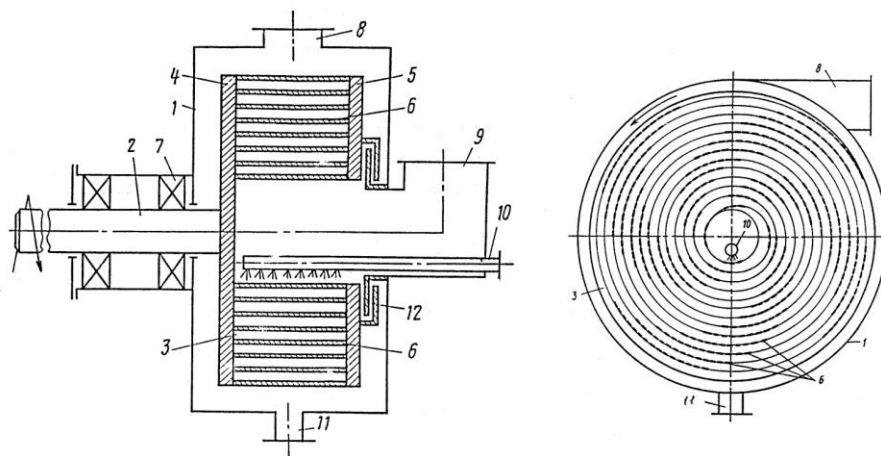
Скоростной роторный центробежный теплообменный аппарат [85]. 1 – корпус; 2 – вал; 3 – ротор; 4, 5 – торцовые крышки; 6 – лопатки; 7 – подшипники; 8 – патрубок входа газовой фазы; 9 – патрубок выхода газовой фазы; 10 – патрубок входа жидкости; 11 – патрубок выхода жидкой фазы; 12 – гидрозатвор.
